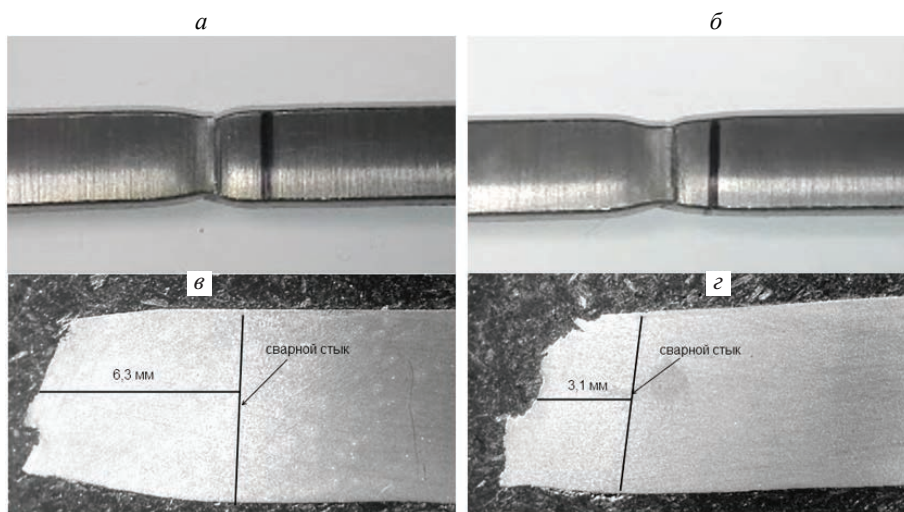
Фотографии образцов сварных соединений после испытаний на статическое растяжение:
